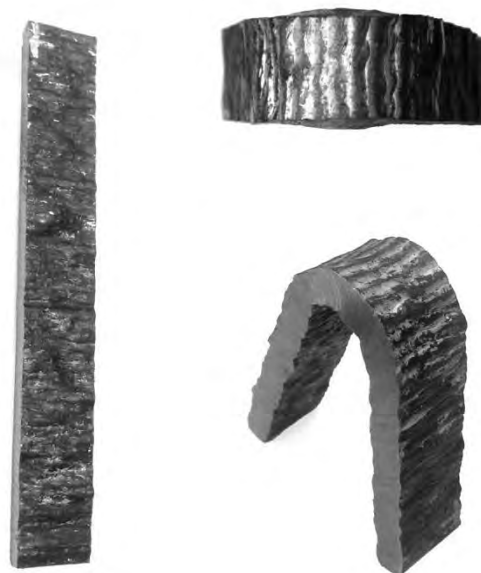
Внешний вид образца до и после проведения испытаний на статический изгиб
